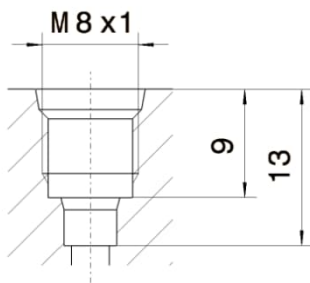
Formbohrung für Gewinde M 8 x 1\
